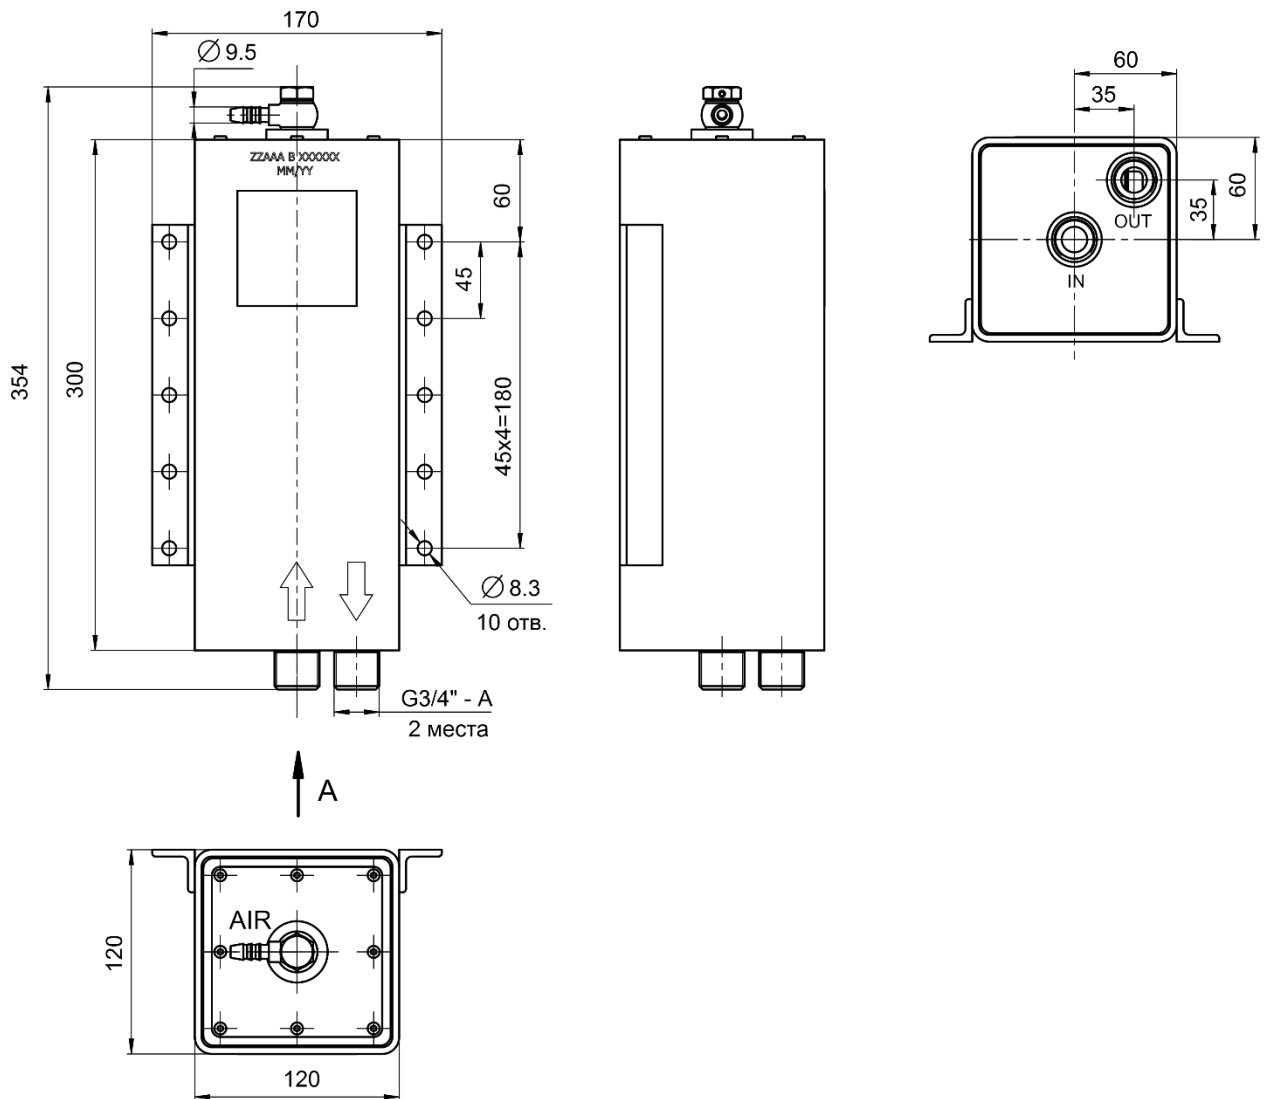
Габаритные размеры [газоотделителя GE](#)
